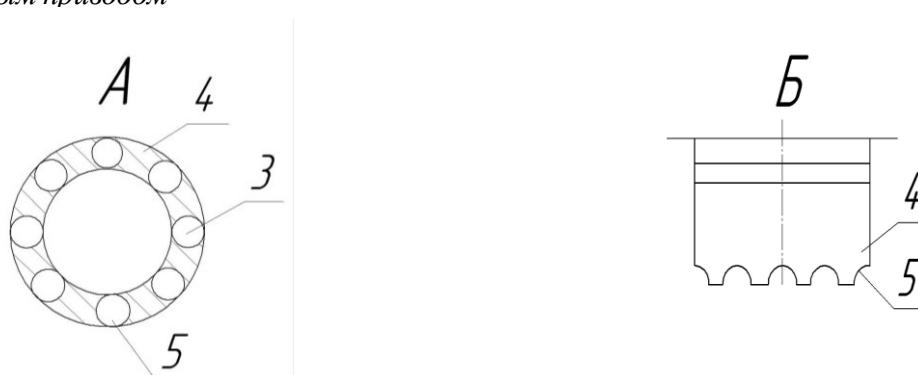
Вид снизу коронки 4 по направлению А Рис. 3. Вид сбоку коронки 4 по направлению Б
